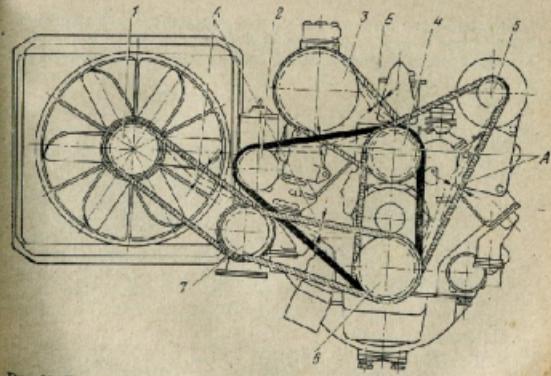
Привод вспомогательных агрегатов двигателя:
